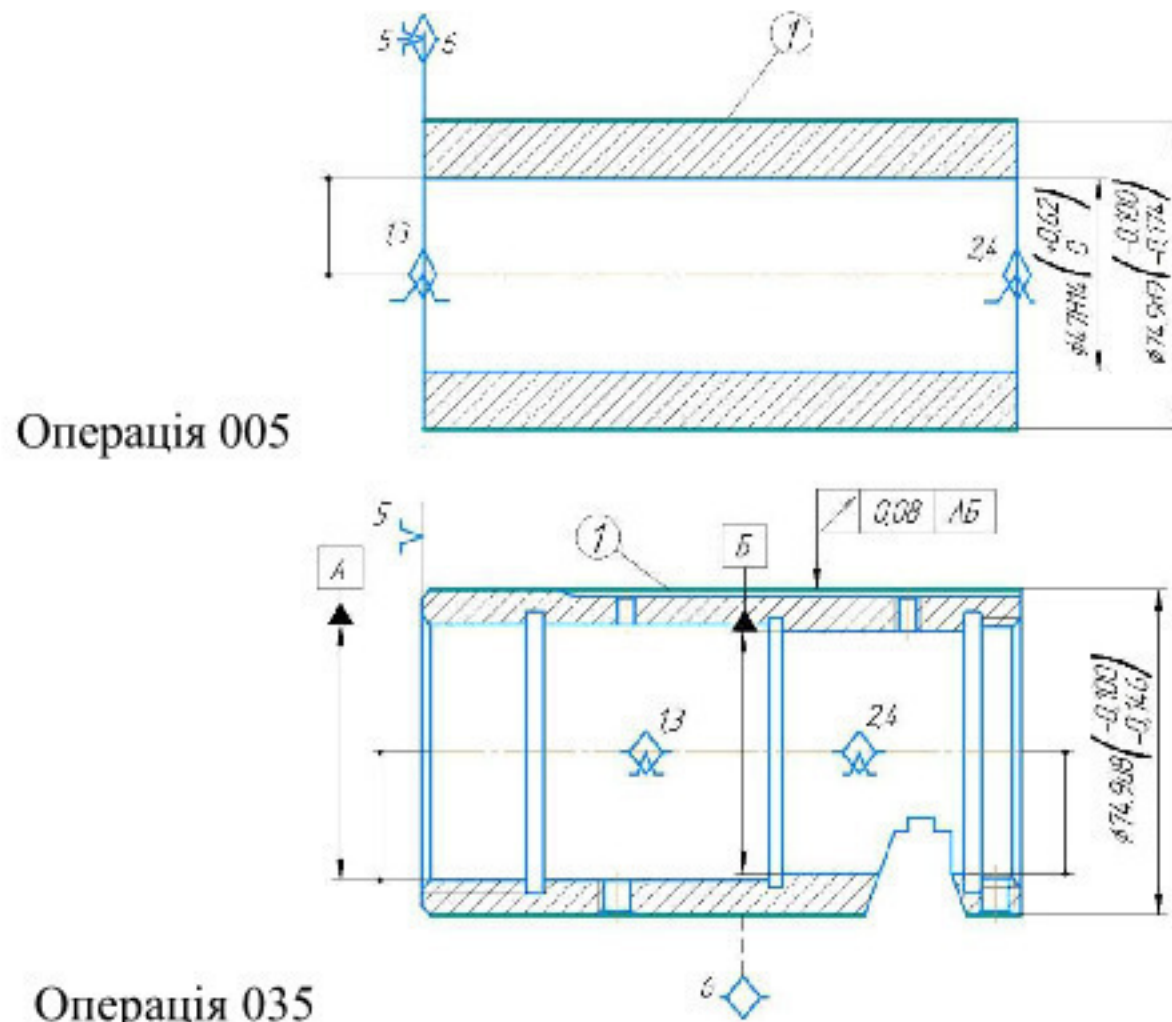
Схема устанавлення і обробки заготовки деталі на операціях 005 та 035
